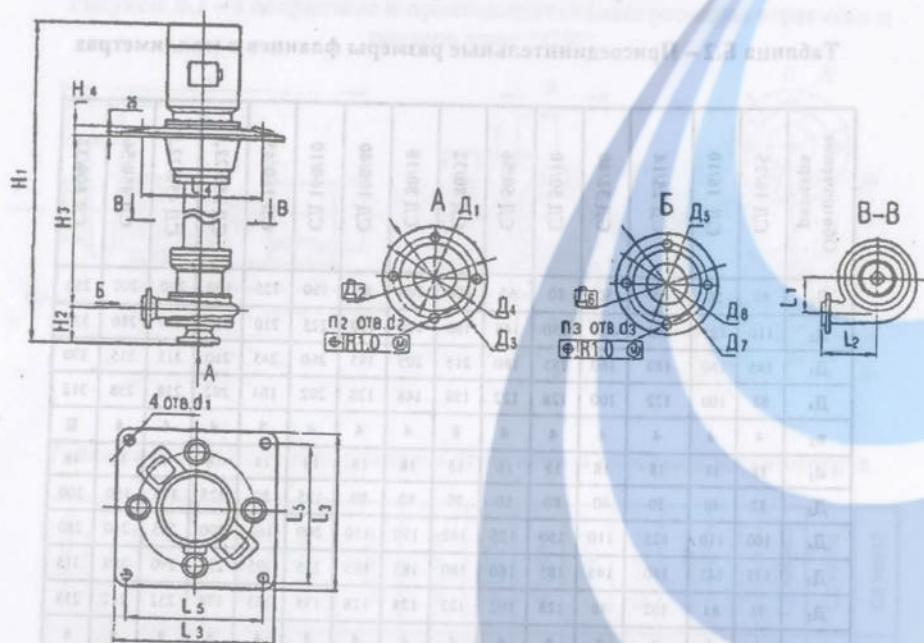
Габаритные и присоединительные размеры агрегатов и насосов типа "СДВ"
